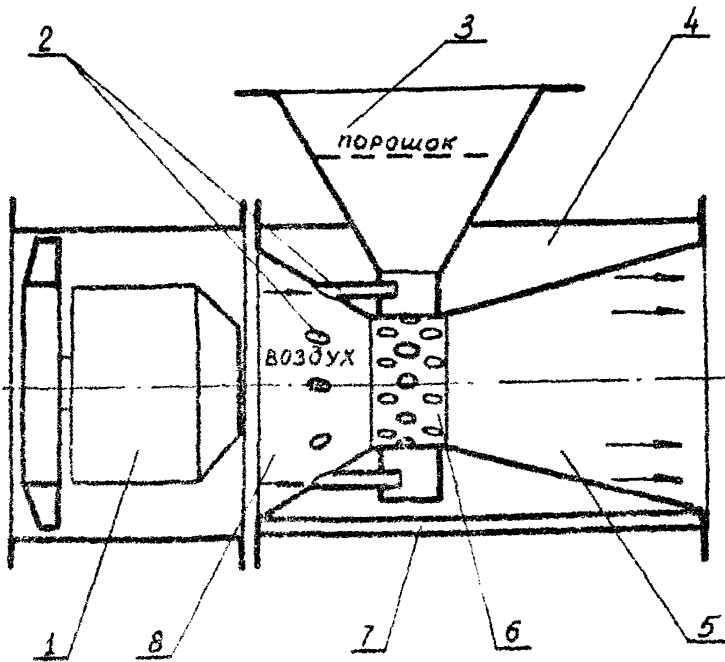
Устройство для создания порошковой струи "Вихрь"
